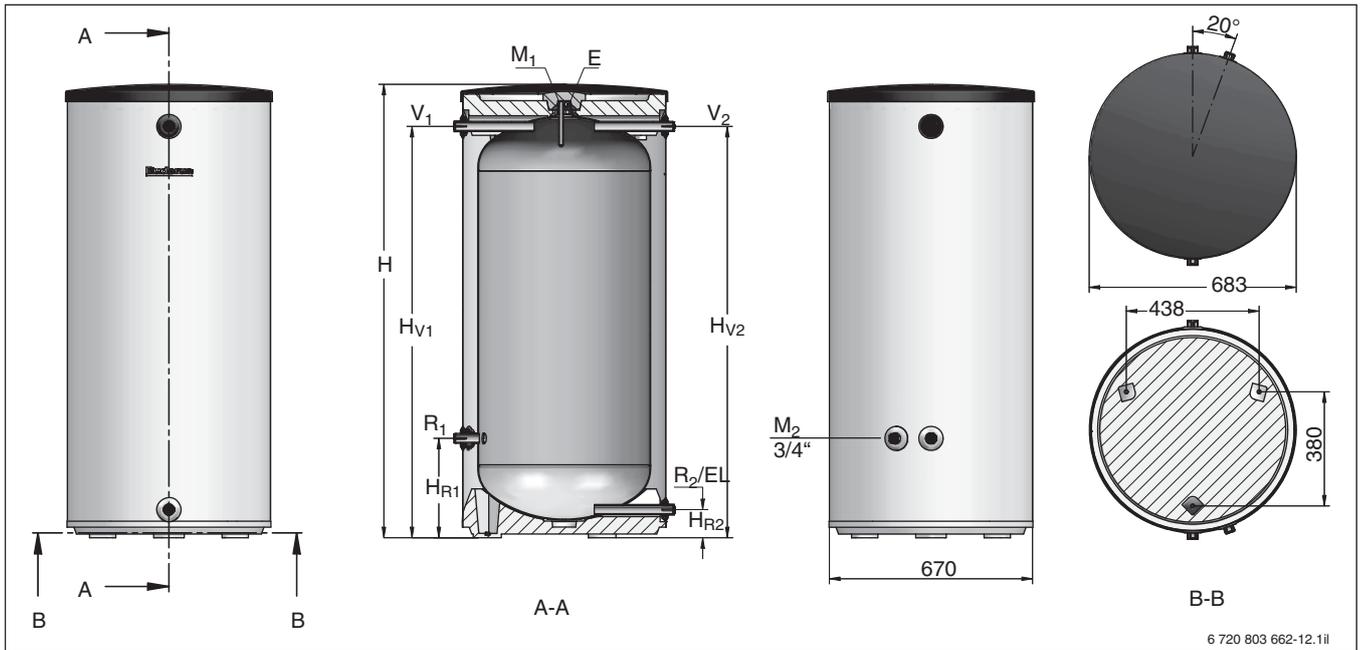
Anschlüsse und Abmessungen Pufferspeicher P200/5 W und P300/5 W (Maße in mm)
